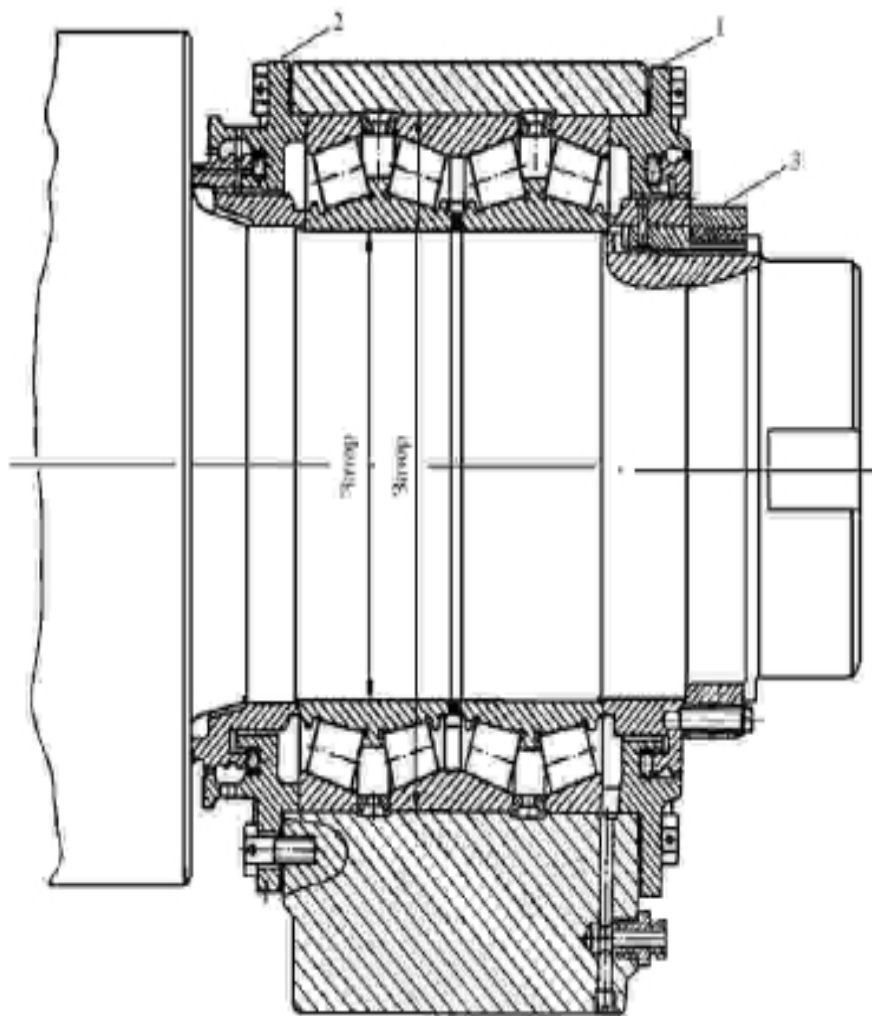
Рабочий валок листопркатного стана горячей прокатки.
